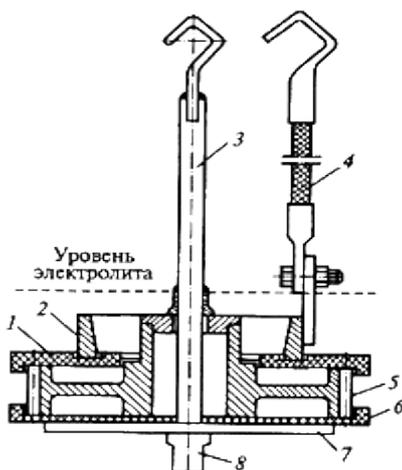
Подвесное приспособление для хромирования ступиц зубчатых колес: 1 - защитный диск из винипласта; 2 - свинцовый анод; 3 - стержень с контактными крючком и фланцем; 4 - гибкий анодный кабель с контактными крючком; 5 - зубчатое колесо; 6 - центрирующий диск нижний; 7 - поджимной фланец; 8 - гайка.
